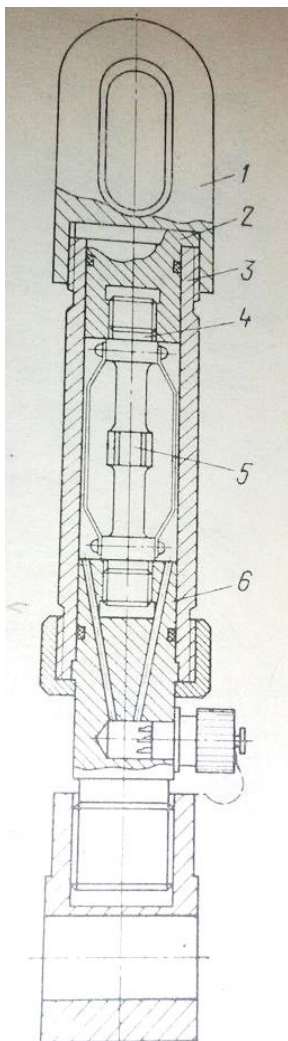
Датчик натяжения кабеля: 1 – проушина; 2 и 6 – пробка; 3 – корпус; 4 – стержень; 5 – тензорезистор
